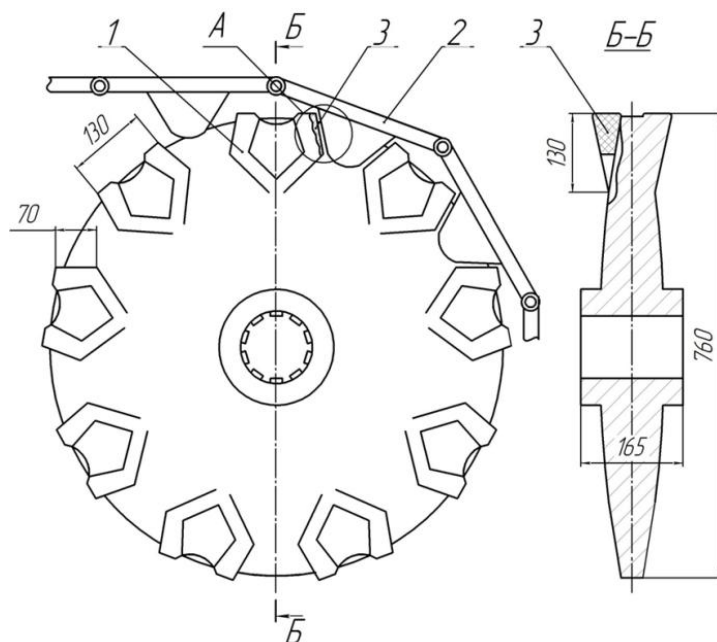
Схема ведущего колеса и его зацепления с зубом гусеницы:
